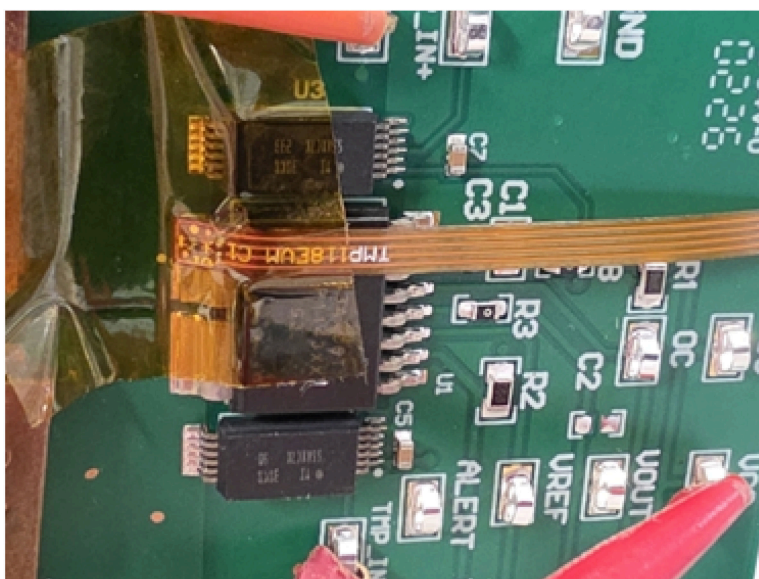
PCB における TMP118 フレックス ケーブルの配置
